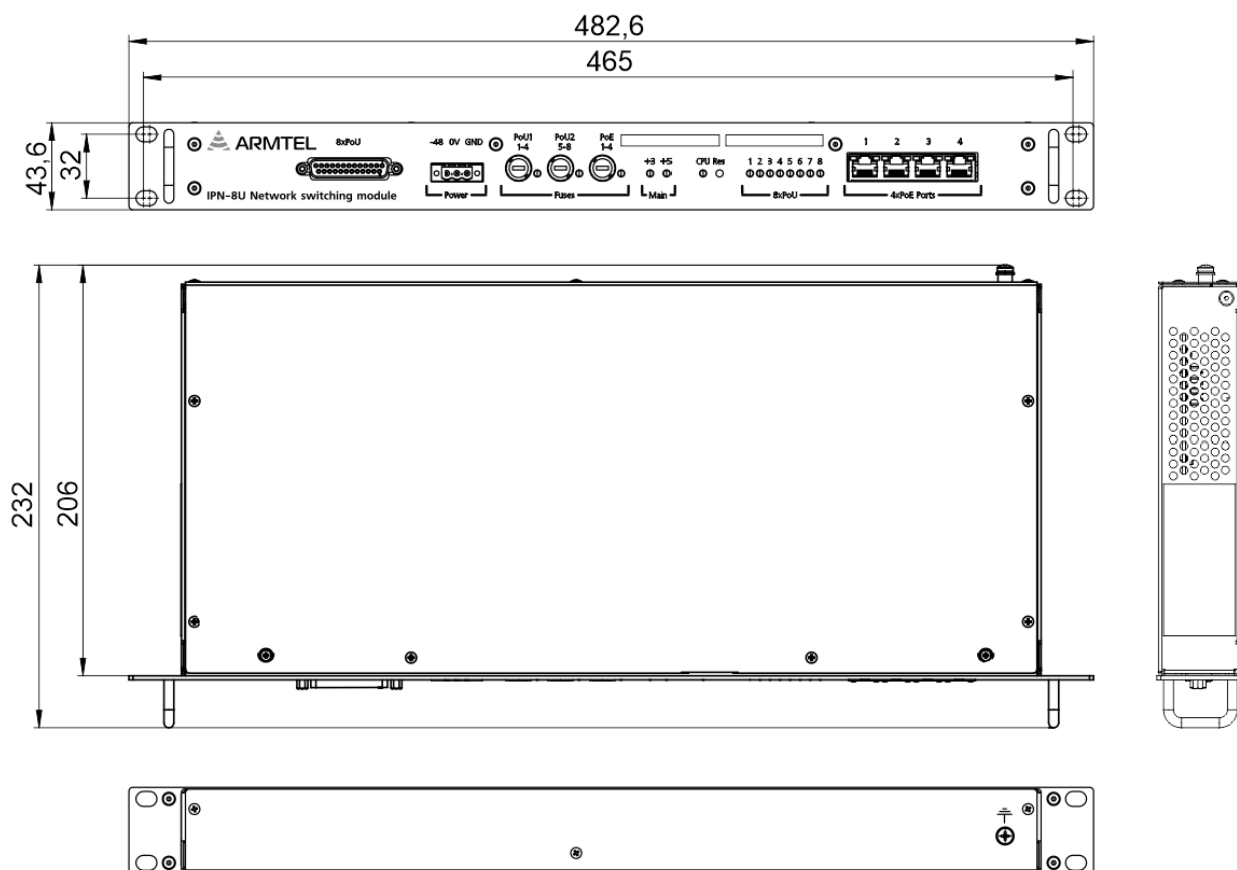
Внешний вид и габаритные размеры IPN-8U
